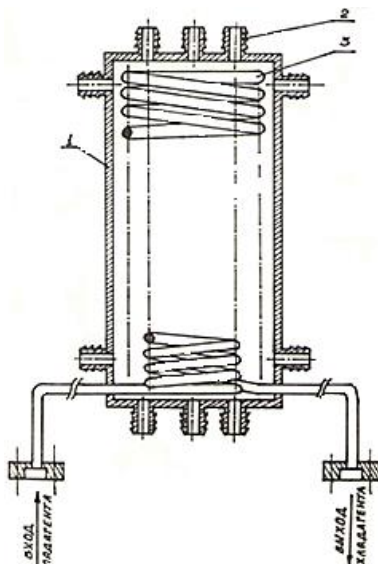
Рекуператор тепла модель №2: 1-корпус; 2 – патрубок; 3 – змеевик.
